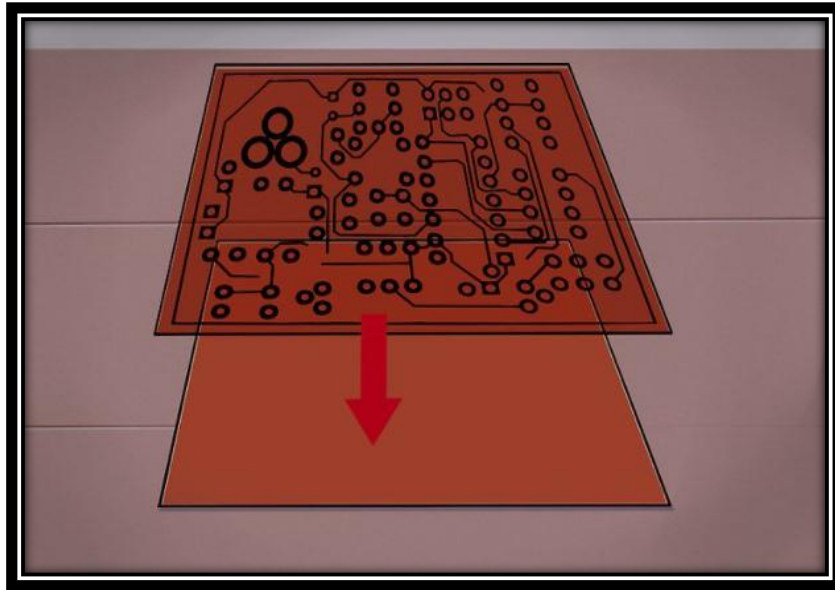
Impression du schéma de PCB sur la plaque FR4 de cuivre.
